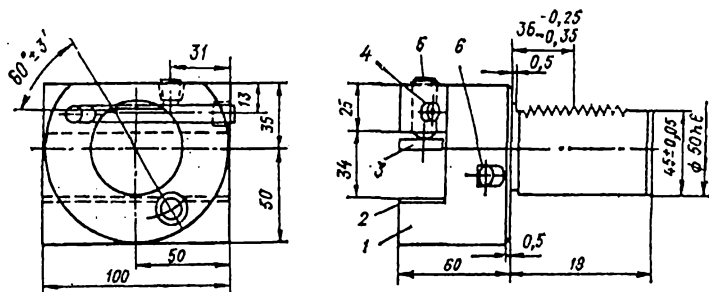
Різцедержатель з циліндричним хвостовиком і пазом для різця
